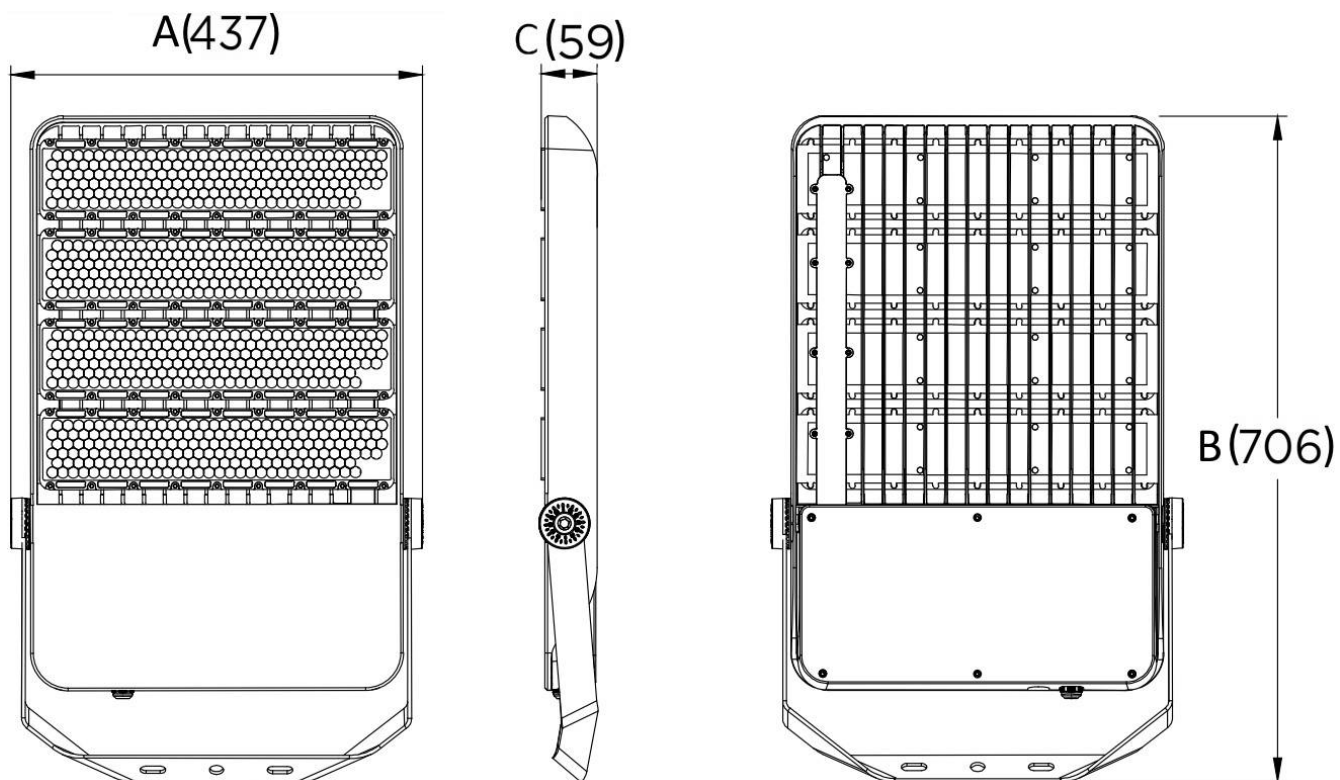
Внешний вид и габаритные размеры прожектора ДО17-600
